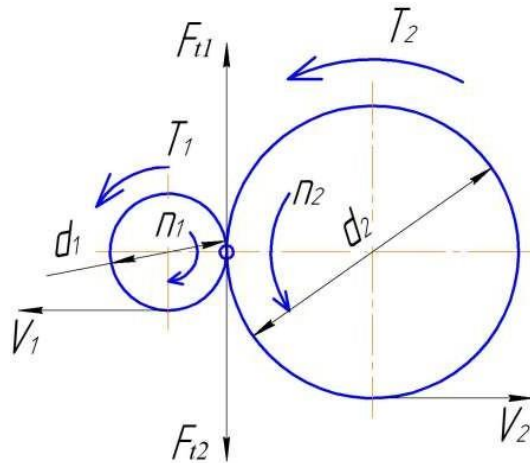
Розрахункова схема передачі обертowego руху
